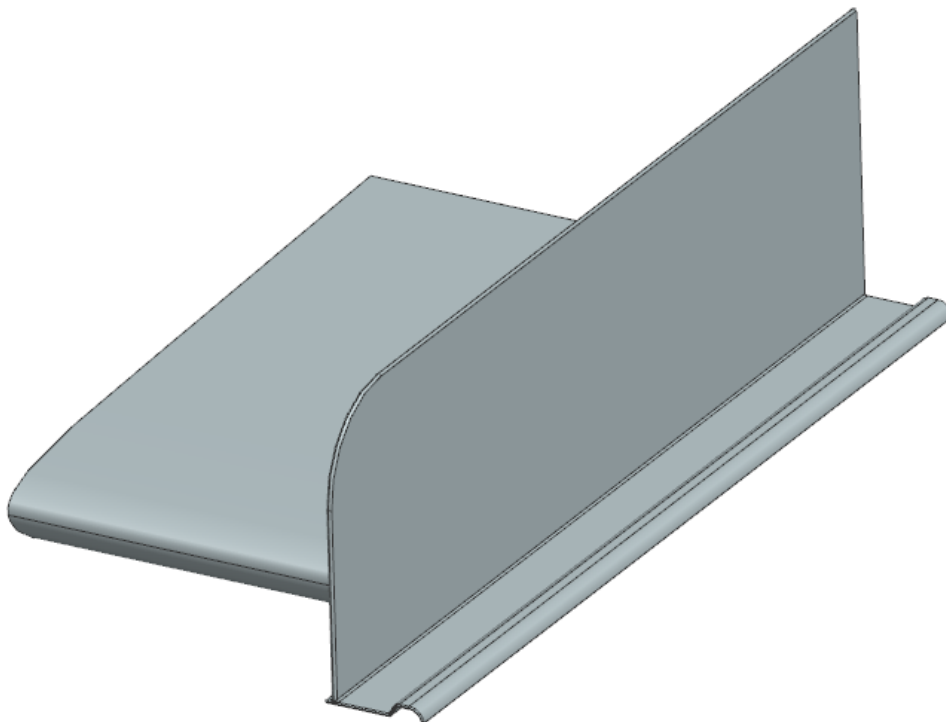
Vista prospettica dell'ENDPLATE 2
